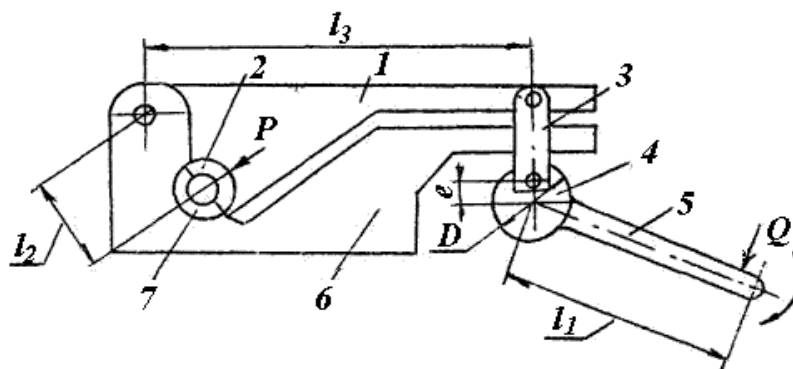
Схема зажимного механизма: 1 – подвижный зажим; 2 и 7 – губки; 3 – тяга; 4 – эксцентрик; 5 – рукоятка; 6 – неподвижный зажим
